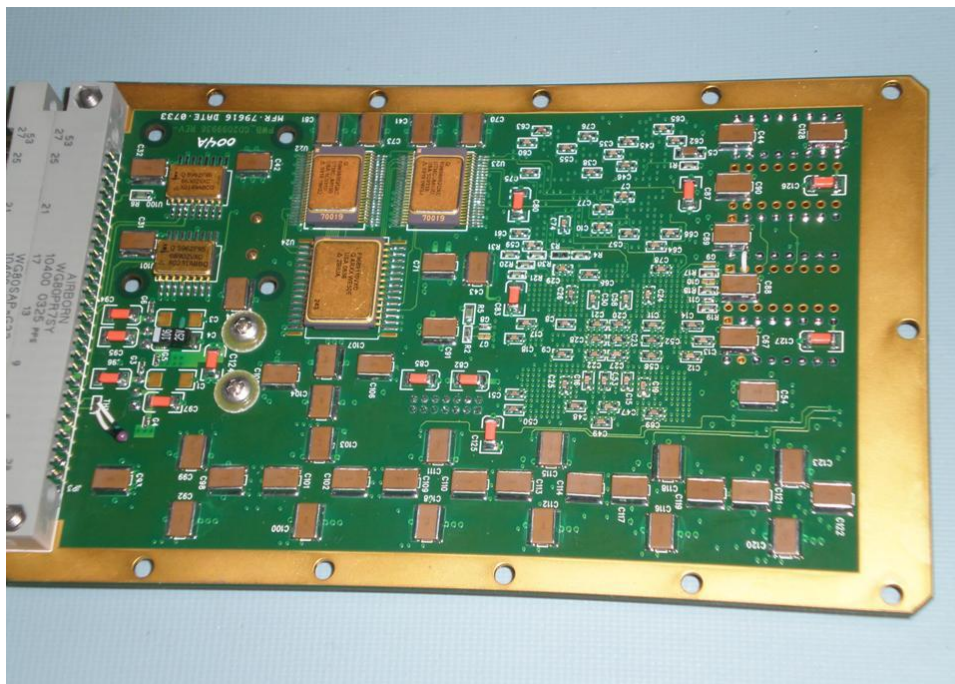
Vue de la face soudure de la carte de vol
